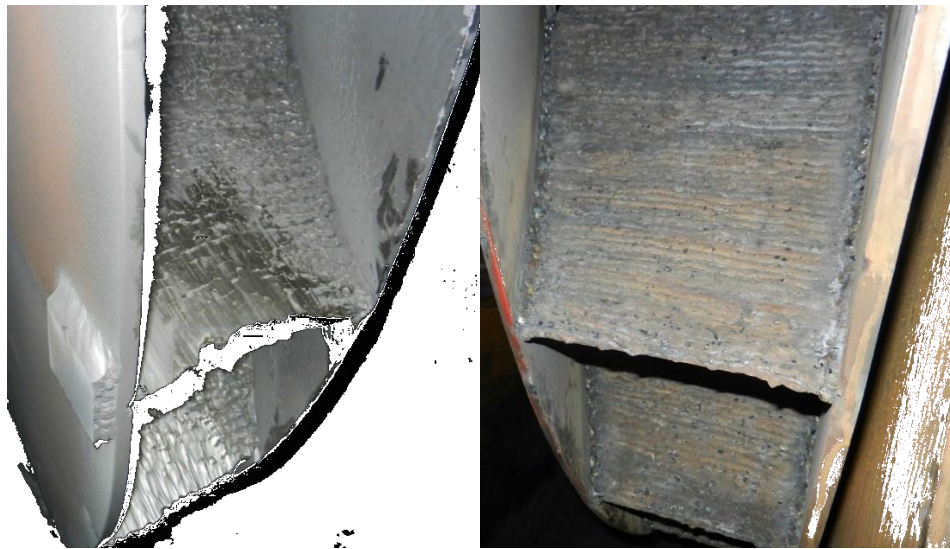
Зліва - Зношена поверхня лопатки робочого колеса млинового вентилятора. Праворуч - Ручна дугова наплавка покритими електродами т-590 на лопатці робочого колеса
